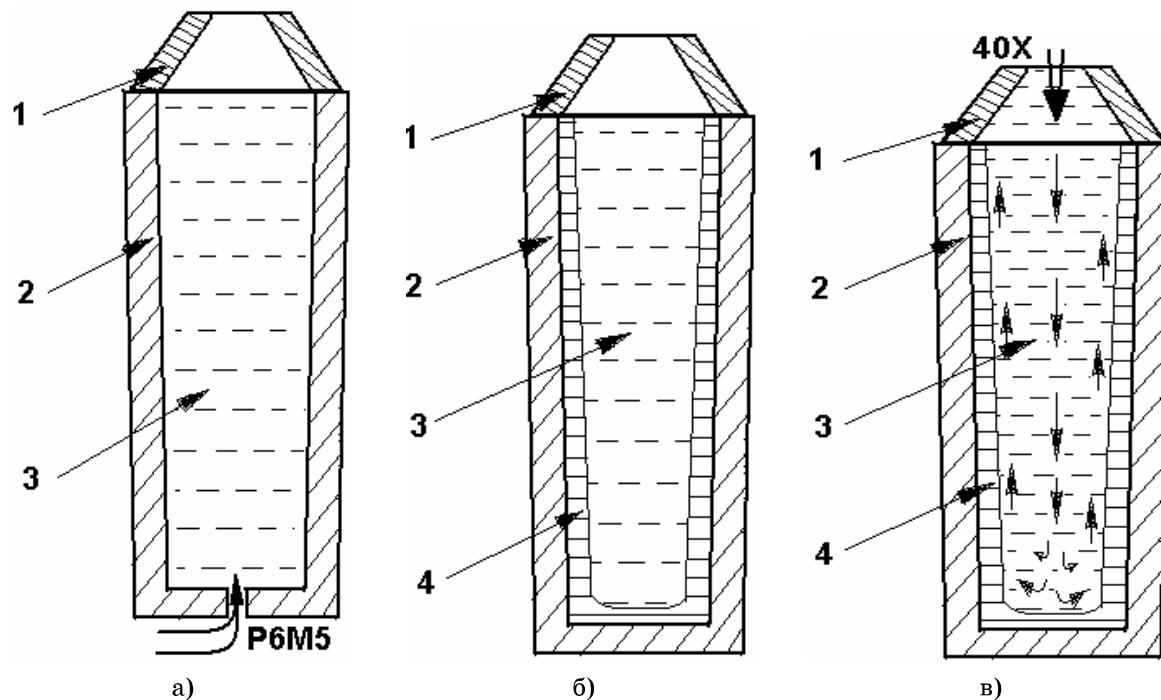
Стадии получения композитного слитка быстрорежущей стали:
